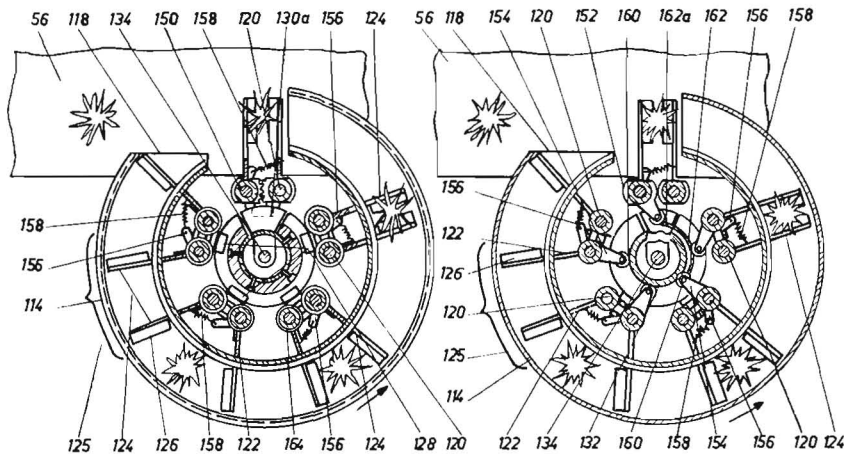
Horizontalschnitte durch einen Pflanzrotor der Maschine nach Bild 4
